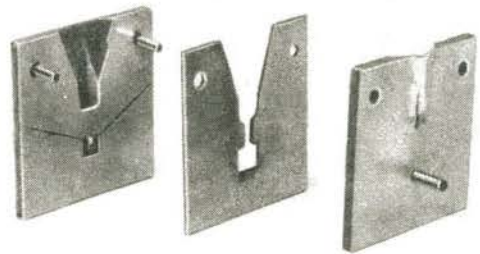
Die Gießform besteht aus drei Blechplatten, in welche die entsprechenden Formen eingearbeitet werden
